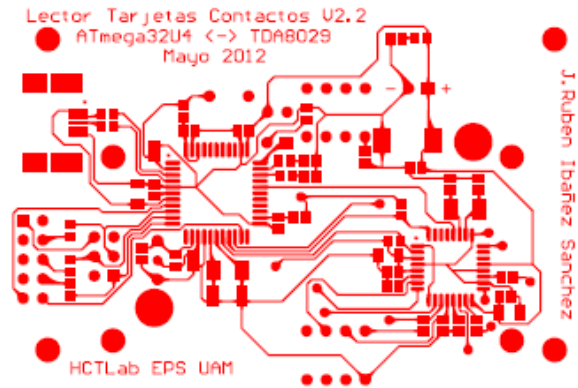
Layout* de la capa superior del PCB a tamaño real.
